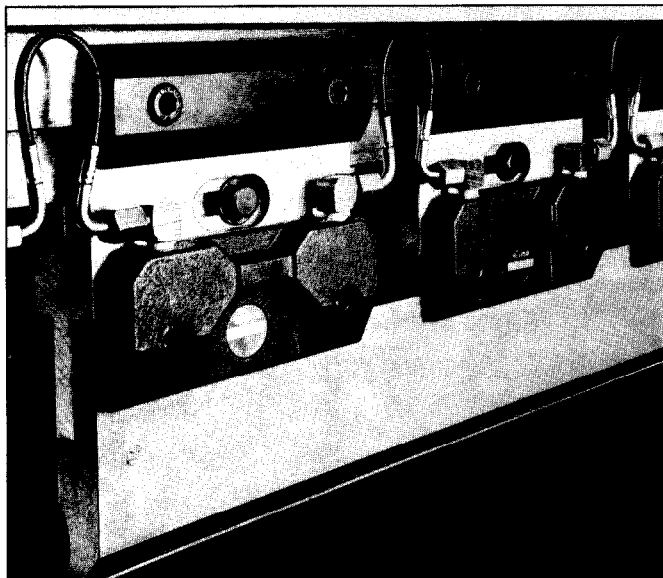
Flachspanner für Abkantpressen mit gesenkschmiedeten Körpern
